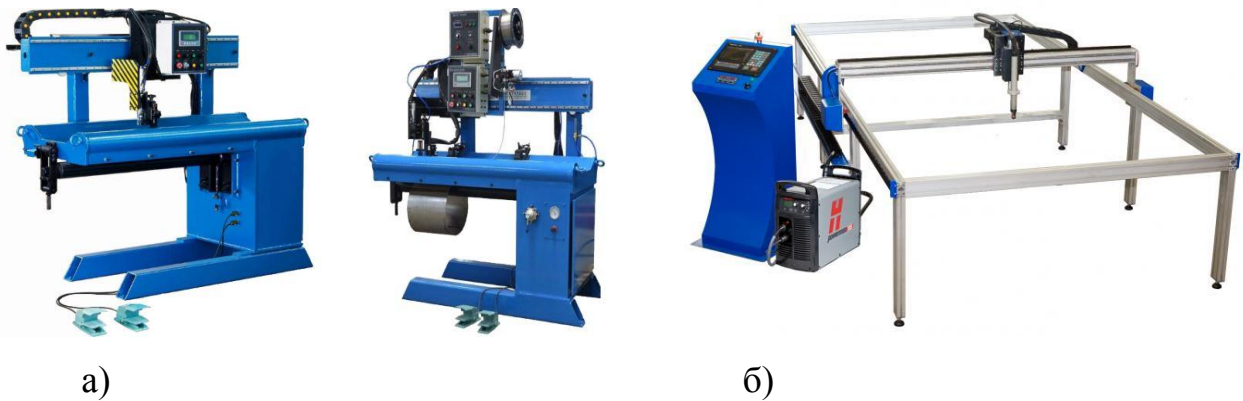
Установки для виконання прямолінійних зварювальних швів:
